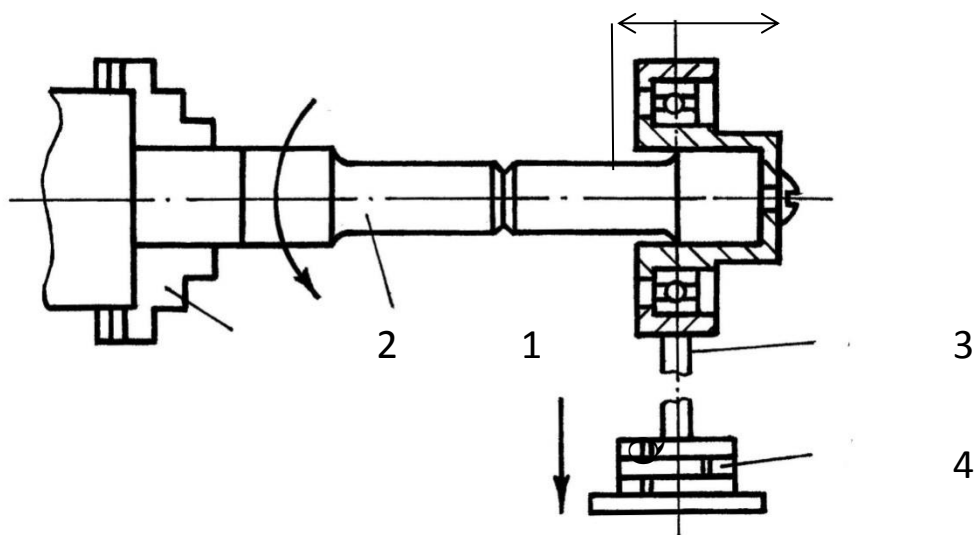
Схема консольного нагружения цилиндрического образца на токарном станке: 1 – образец; 2 – патрон токарного станка; 3 – тяга с шарикоподшипником; 4 – груз (гири).
